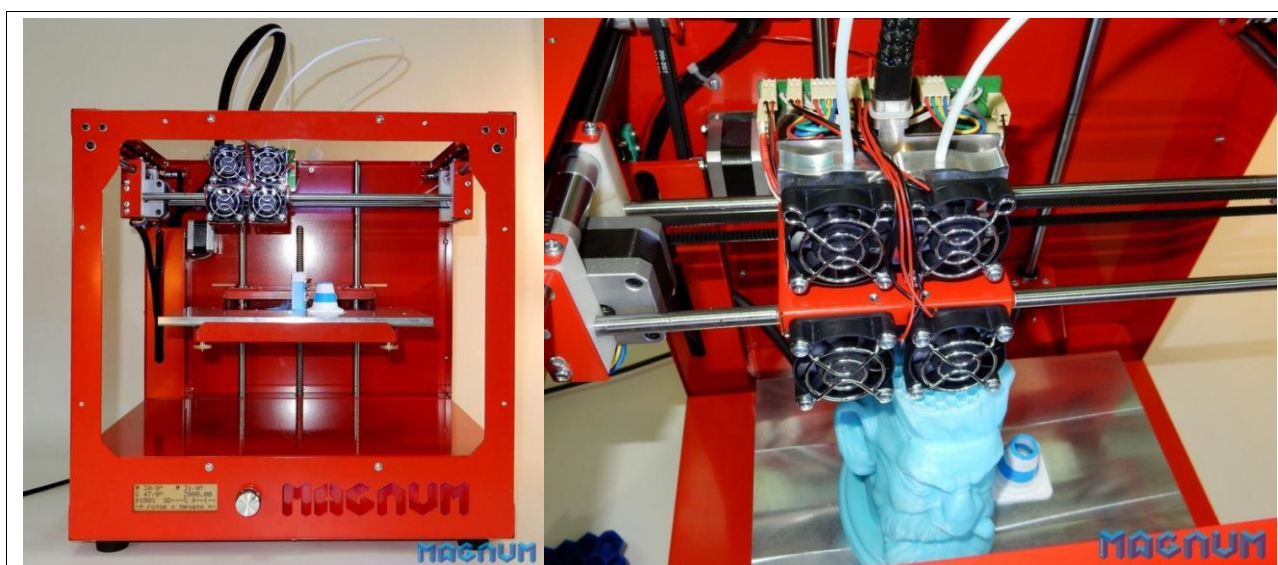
Загальний вигляд принтера з конструкцією кінематики фірми Makerbot
